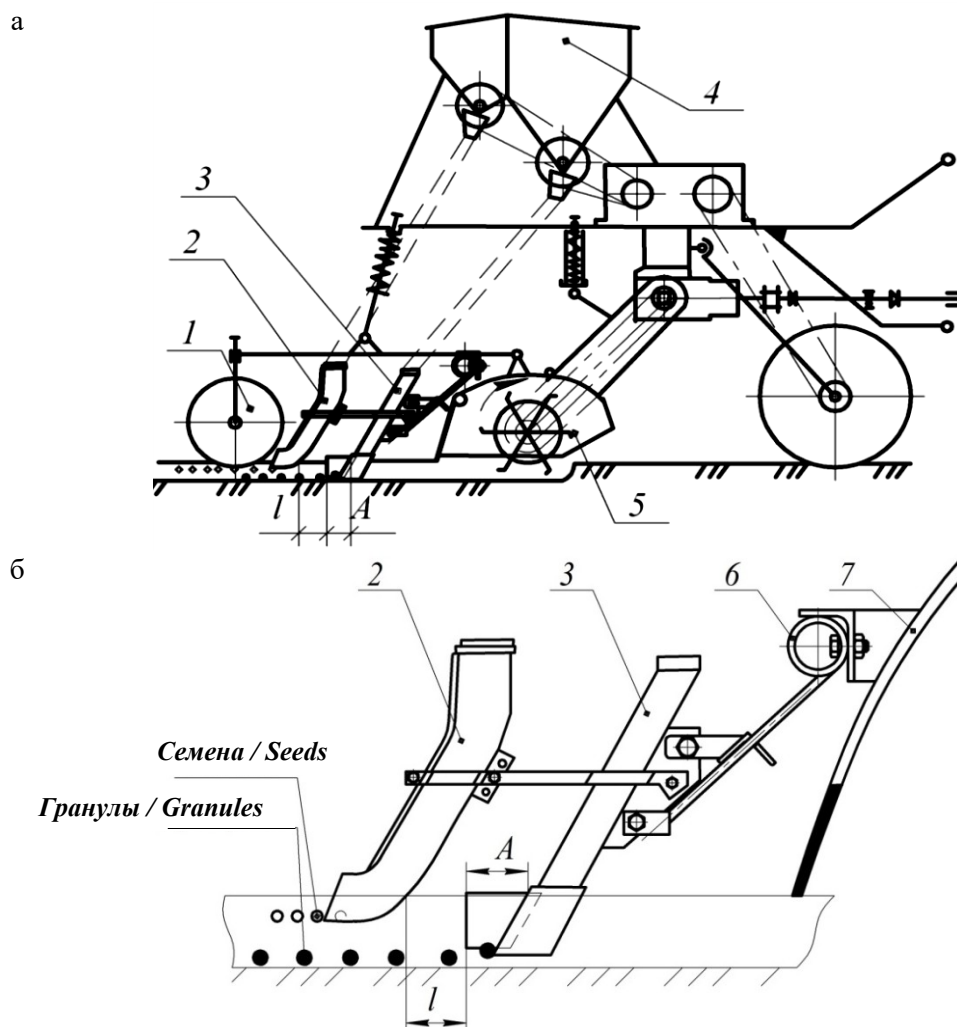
Технологическая схема дернинной сеялки полосного посева (а) и её сошниковой группы (б): 1 – прикатывающий каток; 2 – семенной сошник; 3 – туковый сошник; 4 – зернотуковый ящик; 5 – фрезерный бороздовскрыватель; 6 – механизм подвеса сошниковой группы; 7 – защитный кожух /
